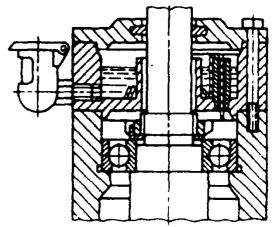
Фитильная смазка подшипников вертикального вала при верхнем расположении резервуара
